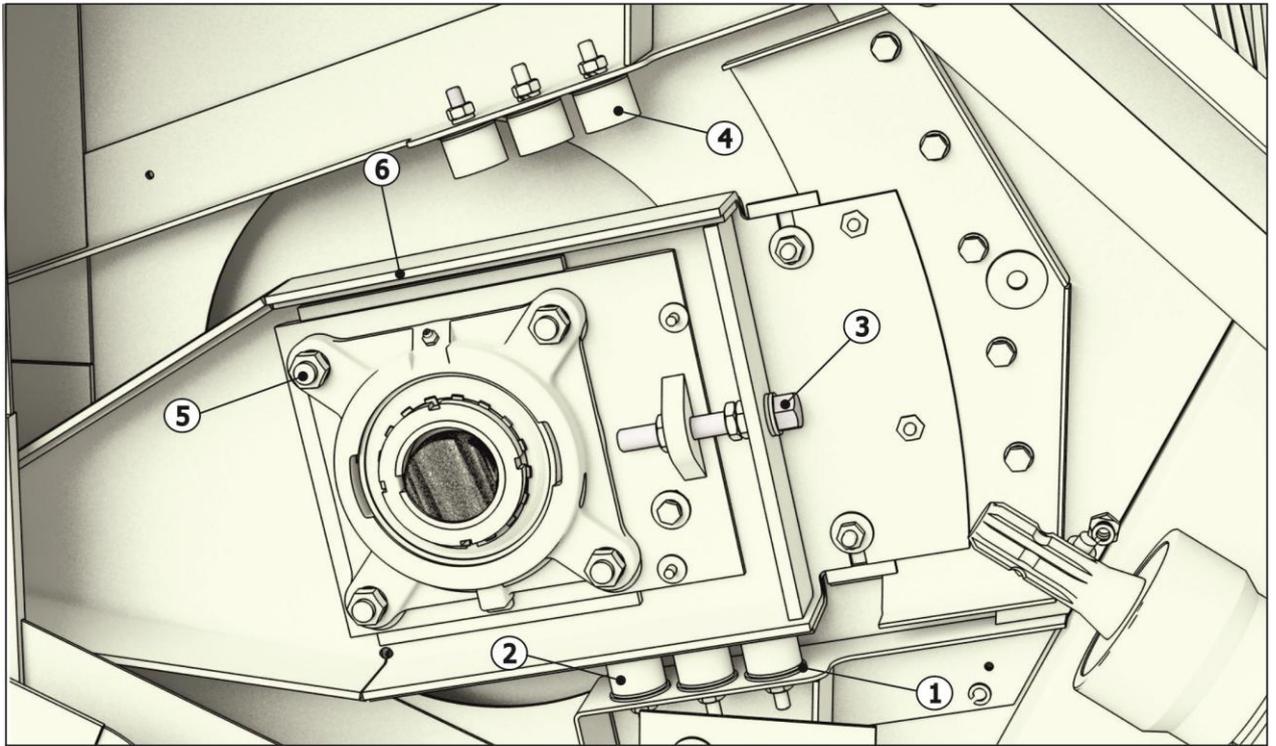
Установка дополнительного регулируемого башмака
